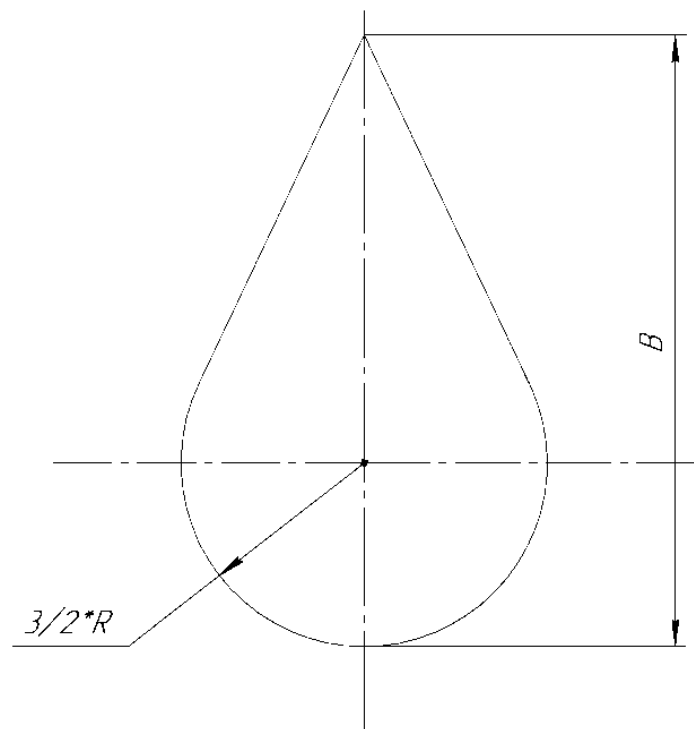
Форма инструмента для формирования отверстий типа TORX
